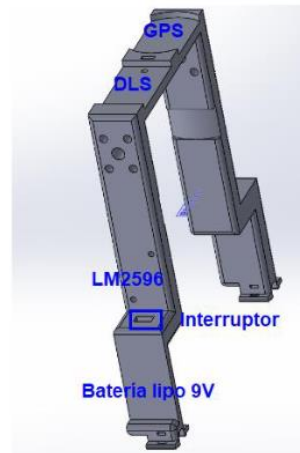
Diseño soporte sensor DLS y módulo GPS. Fuente [86].
